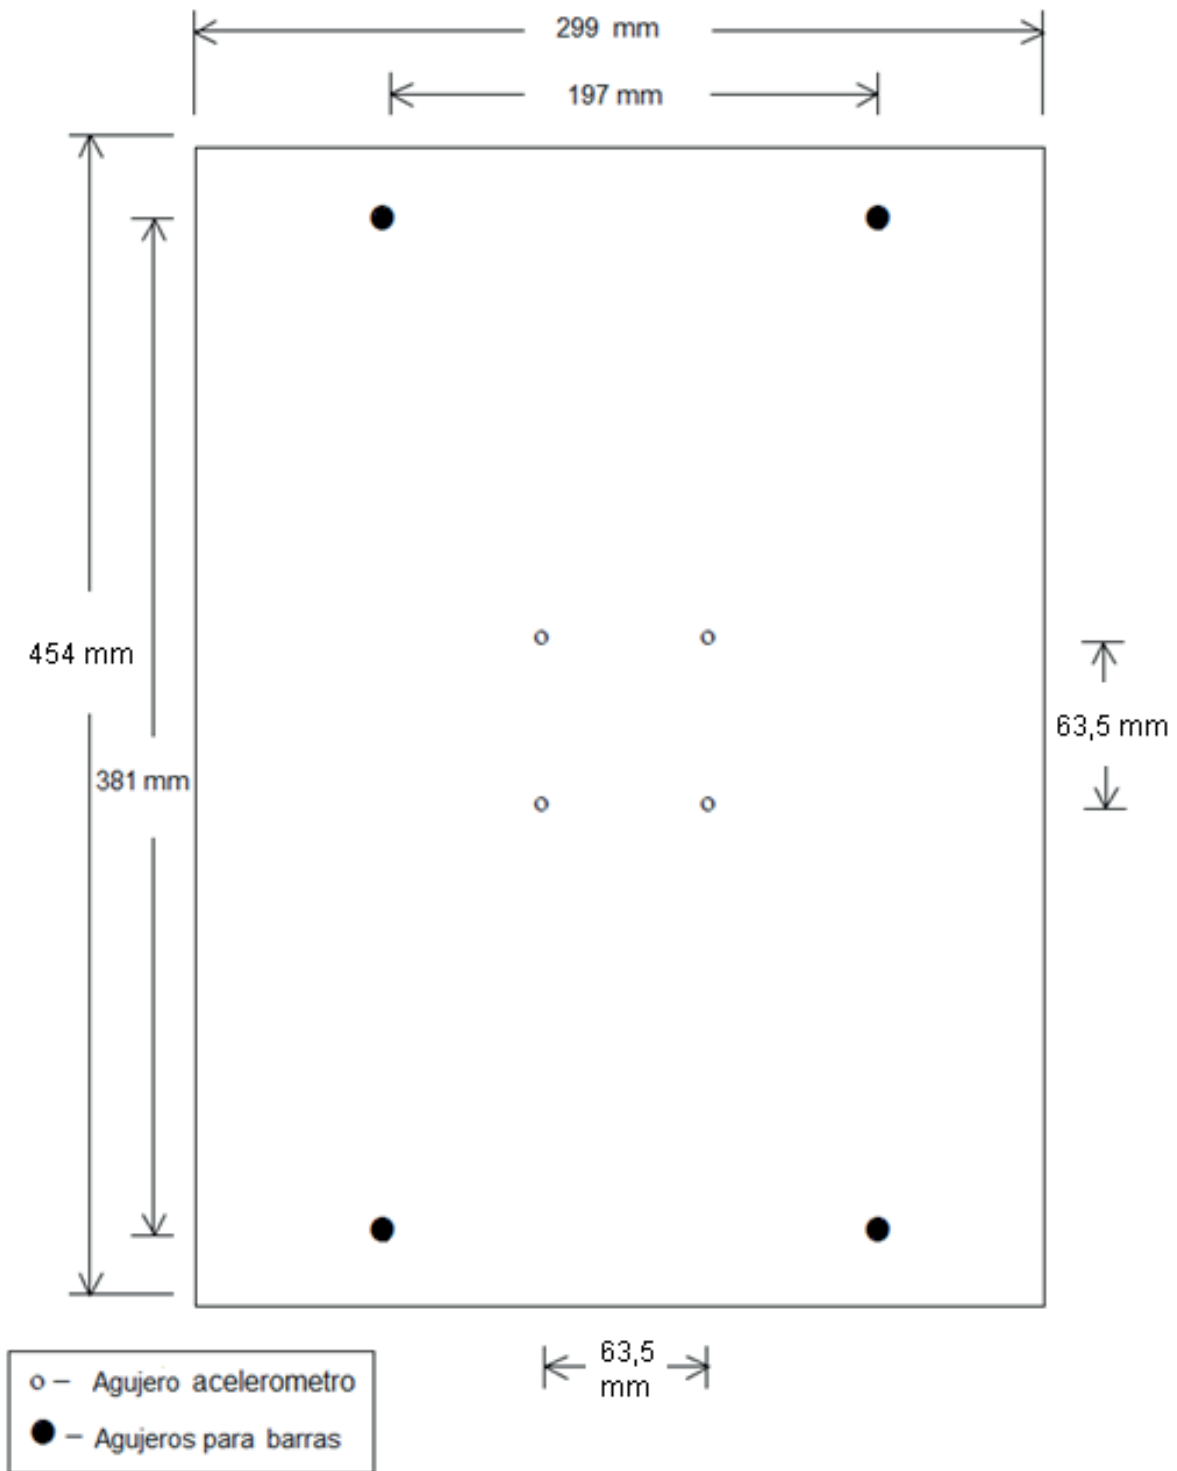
Detalle de conexión entre la placa y la barra roscada
